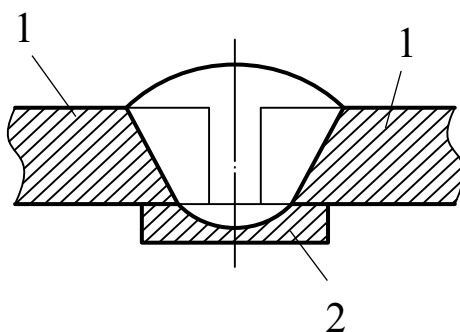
Вид сварного соединения, выполненного на остающейся подкладке: 1 – свариваемые пластины; 2 – остающаяся подкладка
